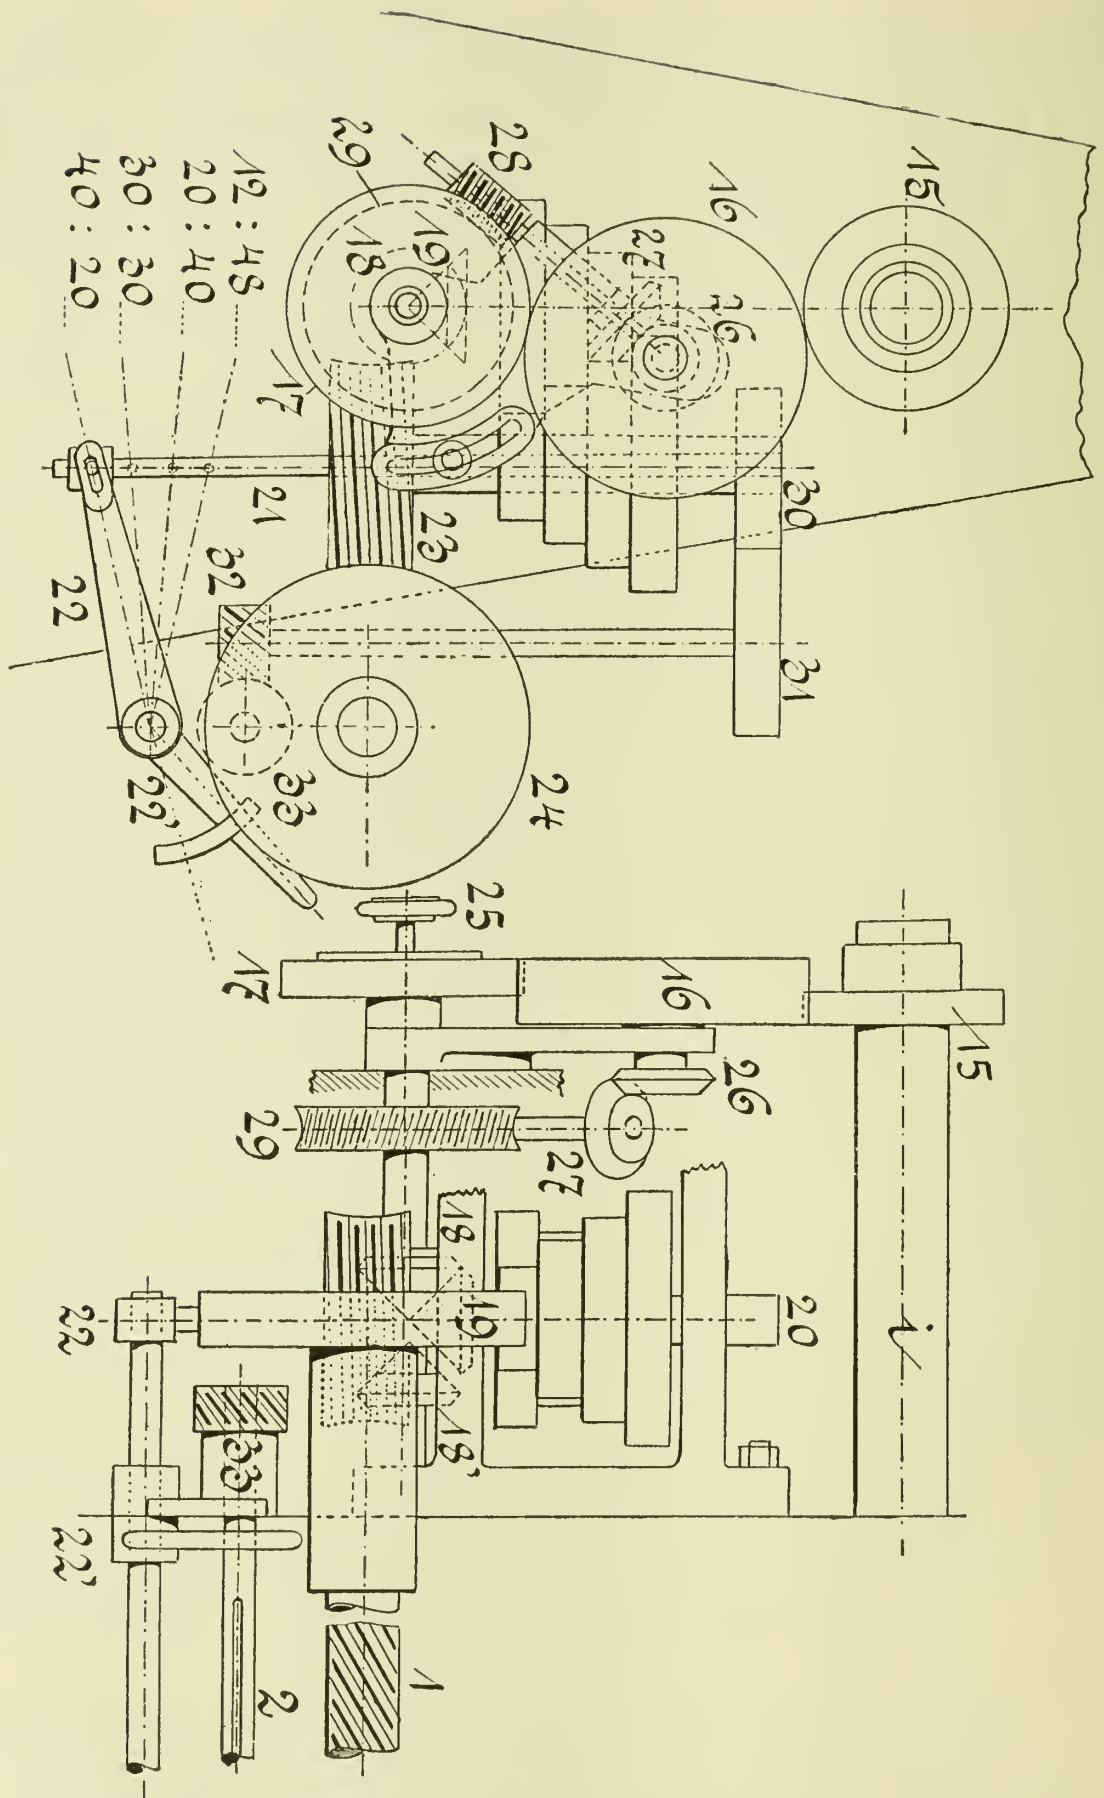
Schaltgetriebe einer Gisholtmaschine.
